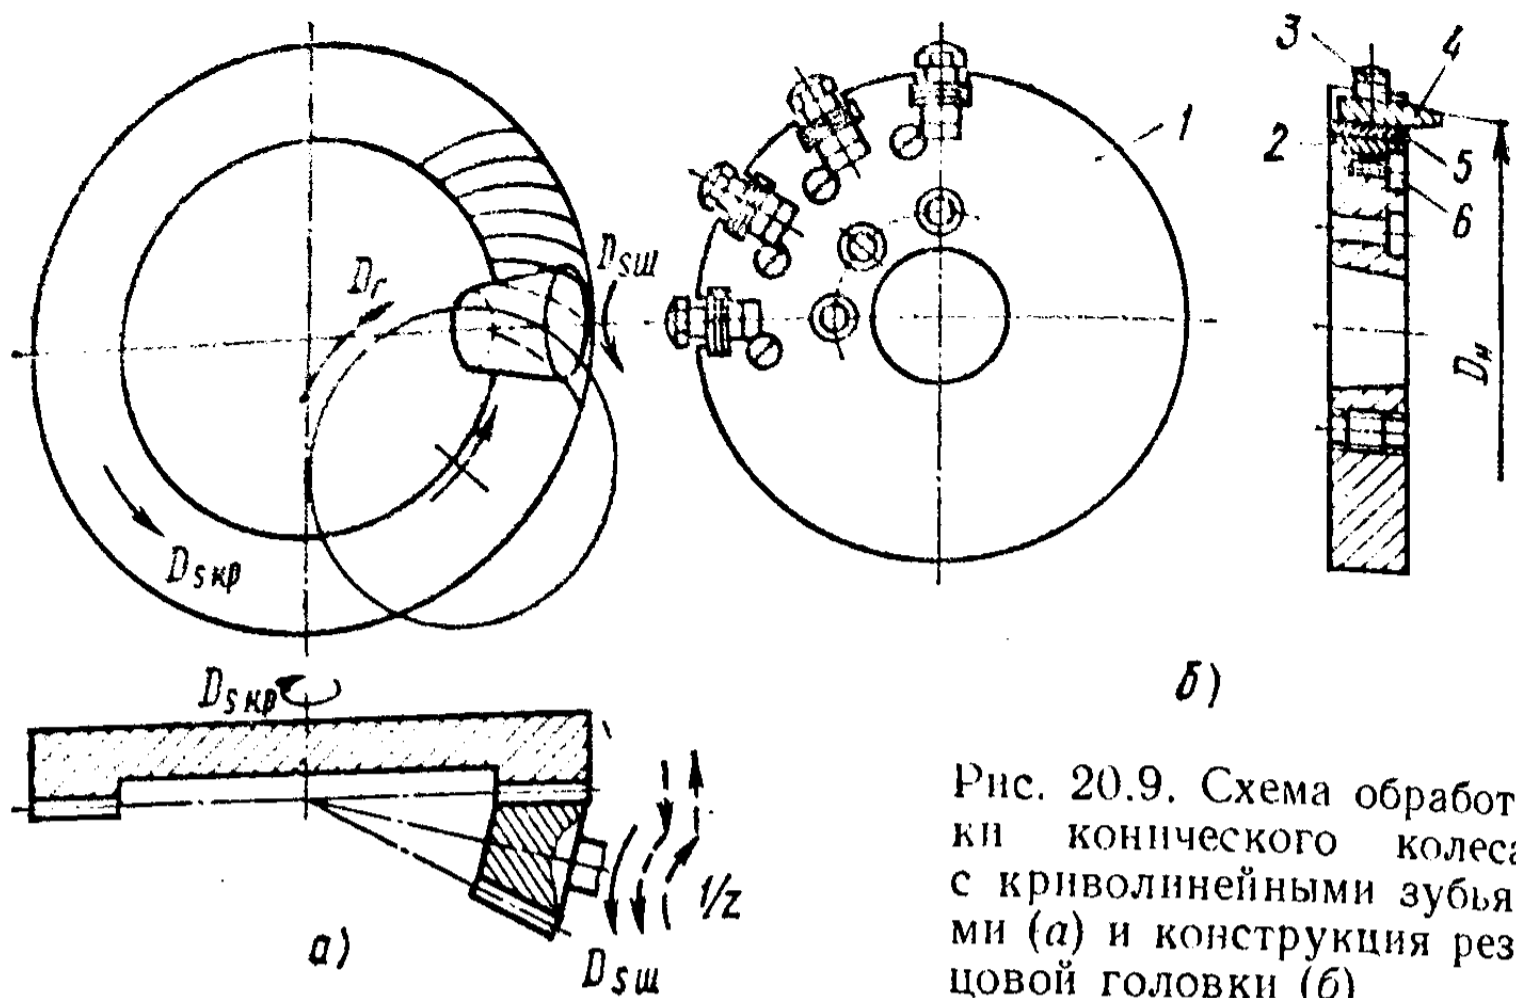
Схема обработки конического колеса с криволинейными зубьями (а) и конструкция резцовой головки (б)
